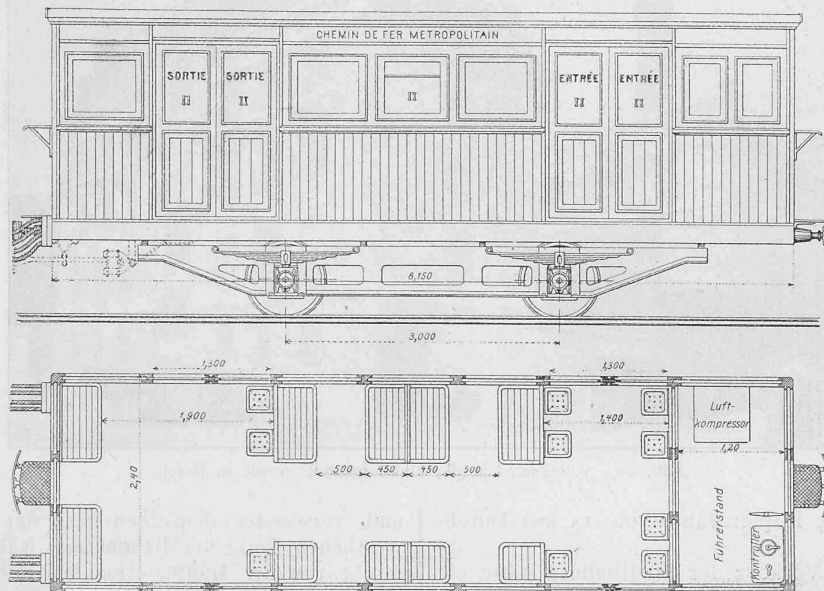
Ansicht und Grundriss der neuen Motorwagen. — Masstab 1 : 75.
